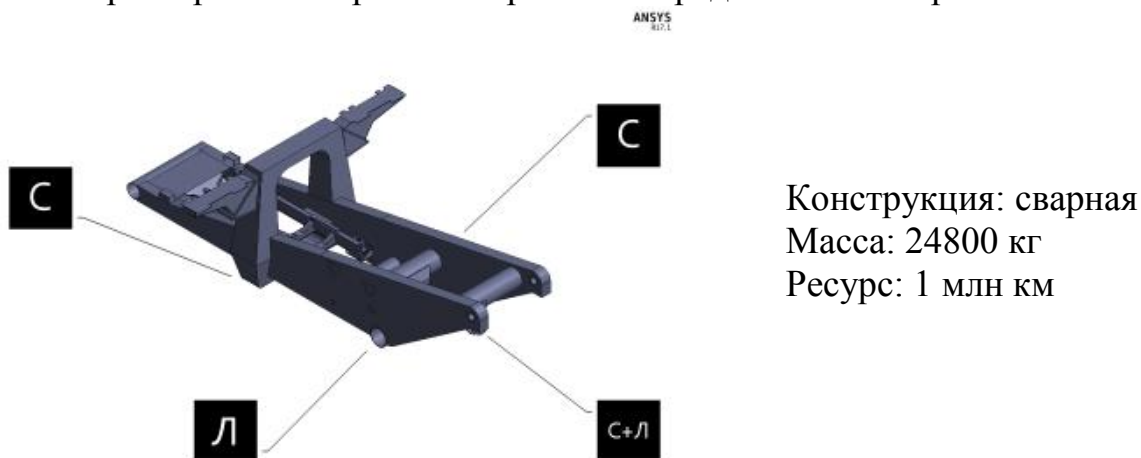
Цифровой прототип рамы к/с БелАЗ 75320: С – сварные детали и узлы; Л – литые детали и узлы
